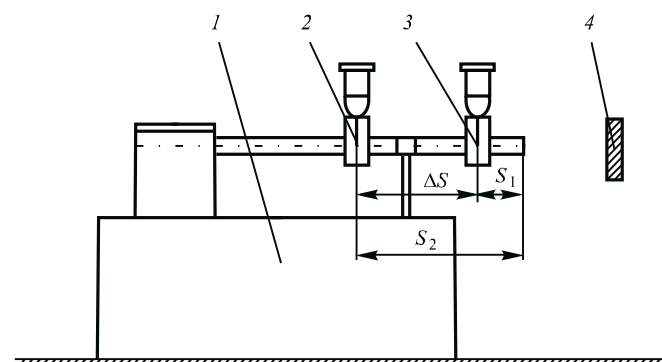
Схема расположения порошковых дозаторов при напылении с синхронной абразивной подготовкой подложки:
